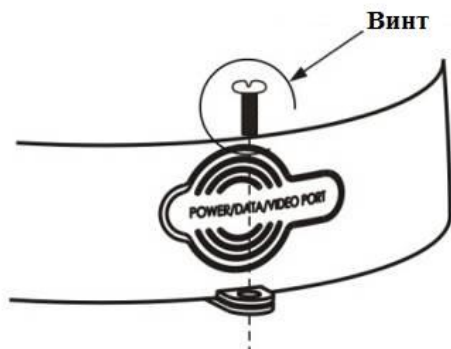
Фиксирование ТКРТЗ-360Т к монтажной площадке
